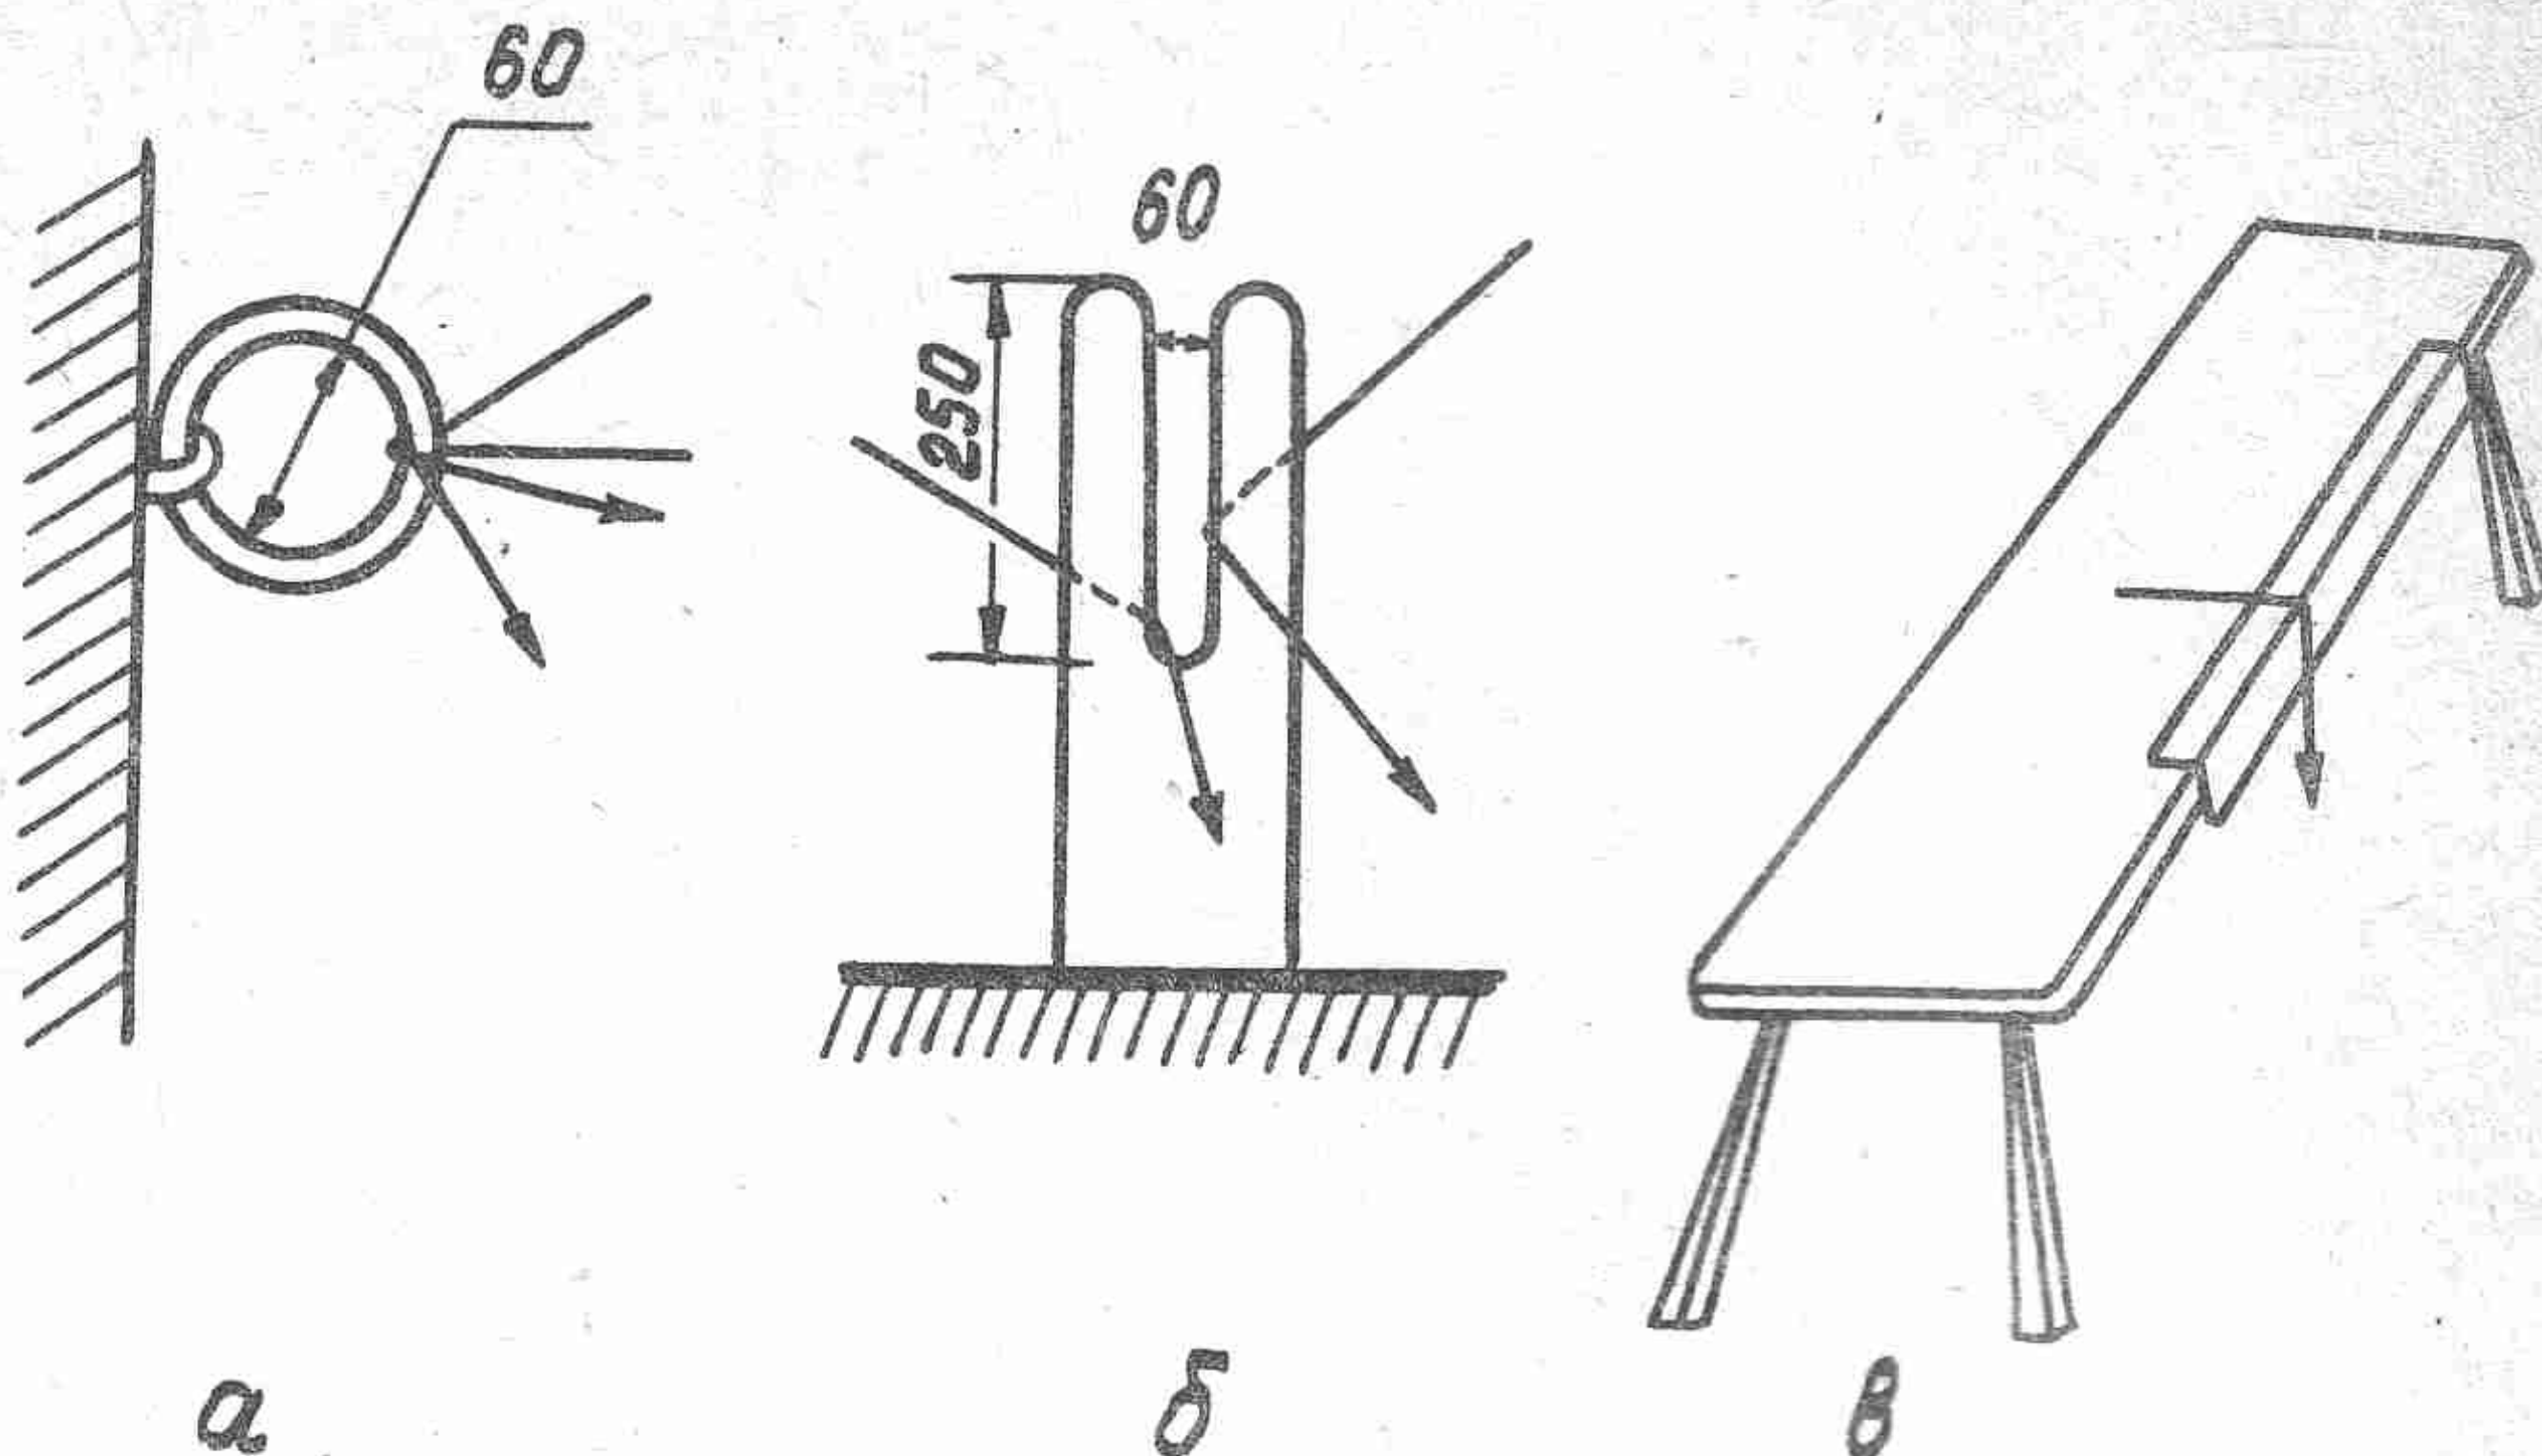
Пристрій для «розбивки» шкури: А — кільце; Б — металева вилка; В — стіл.
